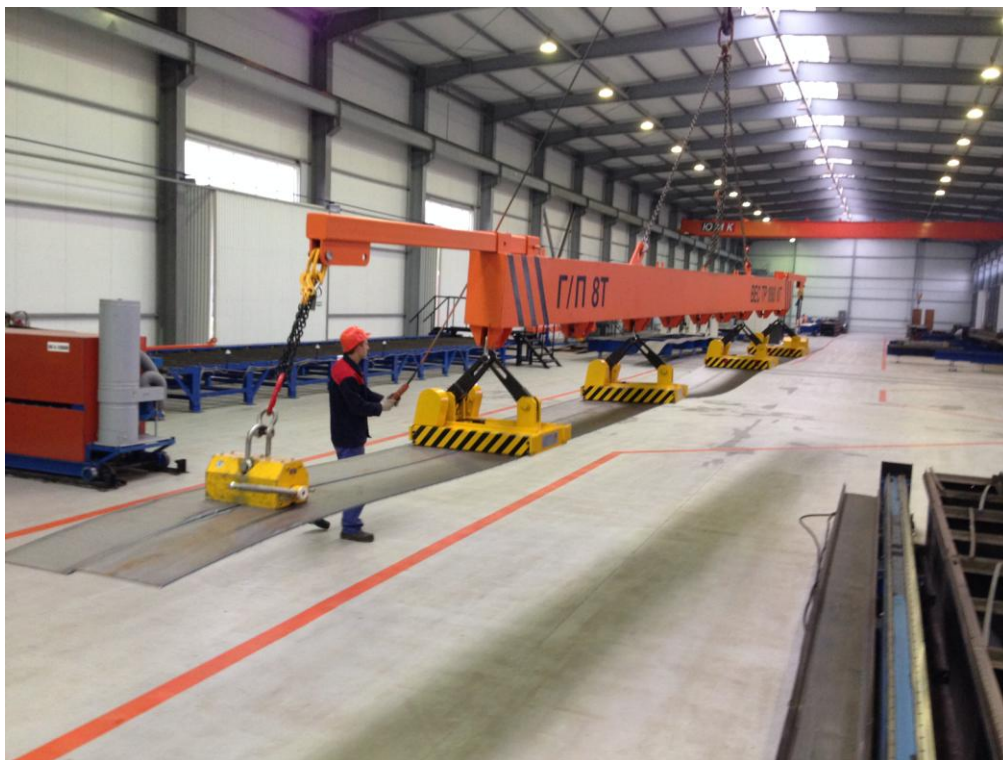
Траверса с магнитными захватами для транспортировки длиномерных полос (стенок и полок сварной балки). С помощью траверсы полосы снимаются со стола линии газовой резки и загружаются в автоматическую линию сварки балок
